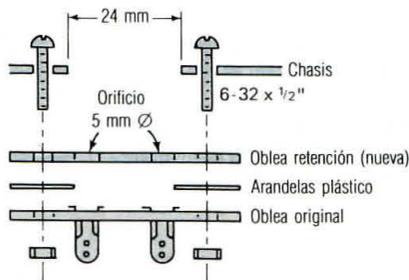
Conjunto del zócalo de bobinas del pequeño medidor por mínimo.
